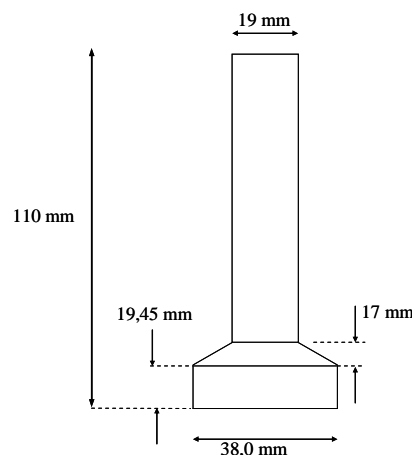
Géométrie et dimensions du piston utilisé pour le test de back extrusion
